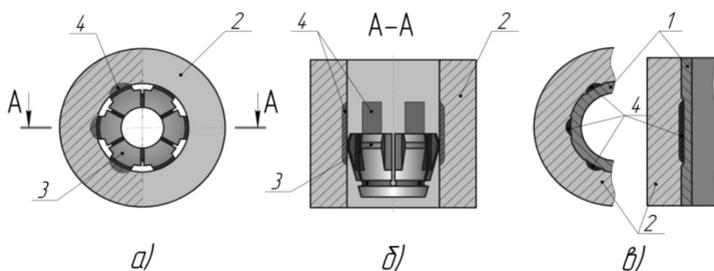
Соединение вал-втулка со сквозными закаленными участками
